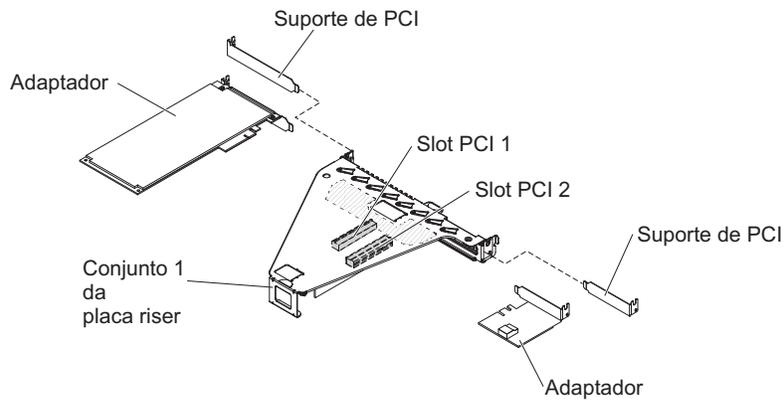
Remoção do Adaptador do Conjunto da Placa Riser PCI 1
